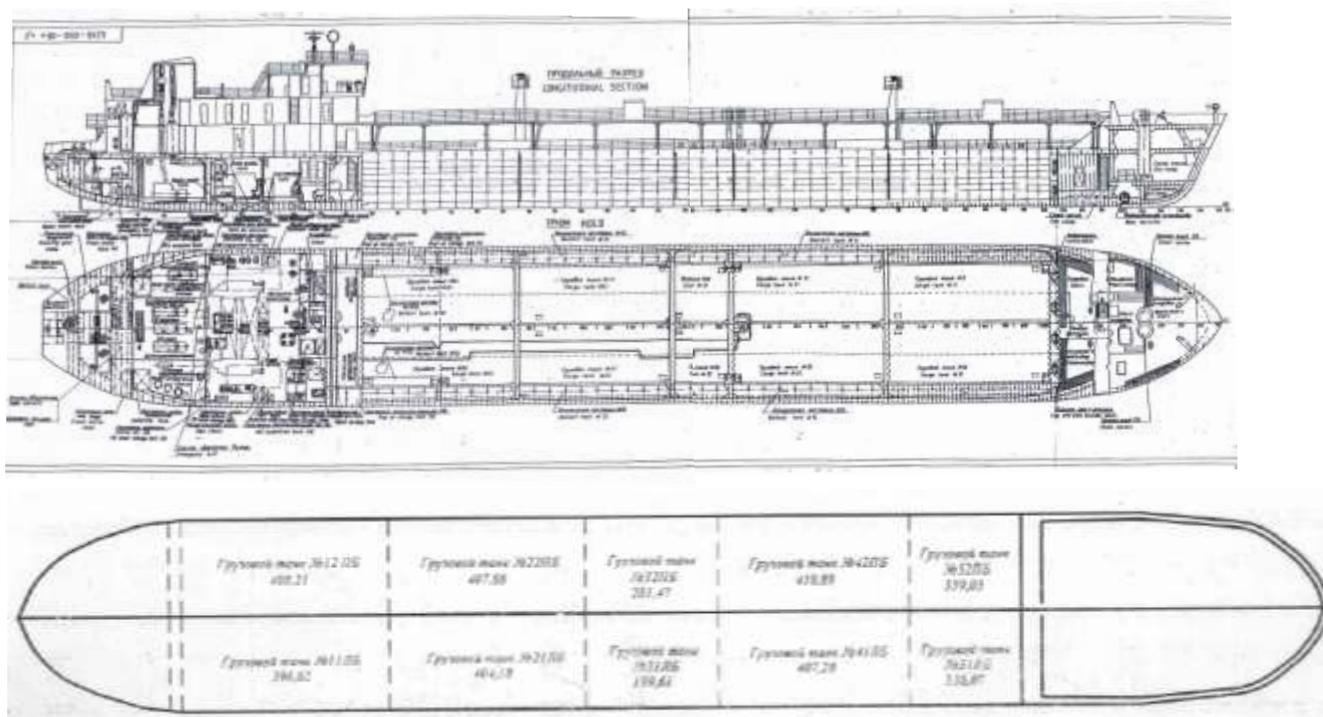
Схема расположения грузовых танков пр. 621
